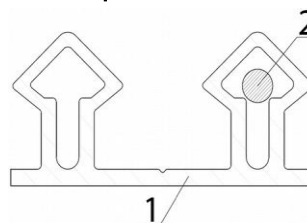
ПЭН уплотнителя двери (устанавливается на этапе изготовления во внутреннем контуре уплотнителя двери)
